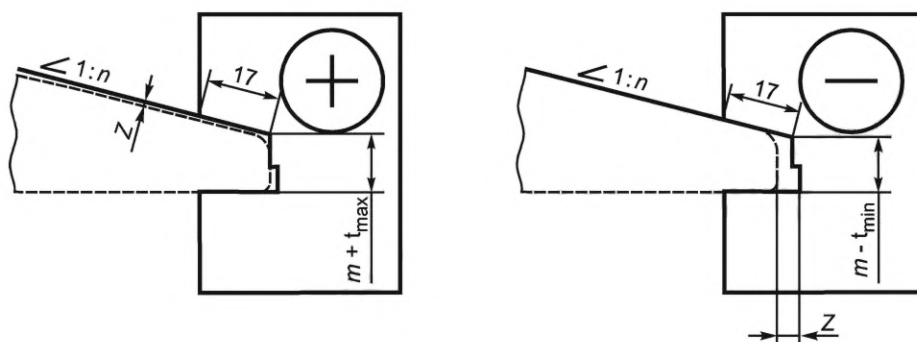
Шаблон контроля ширины головки рельса
